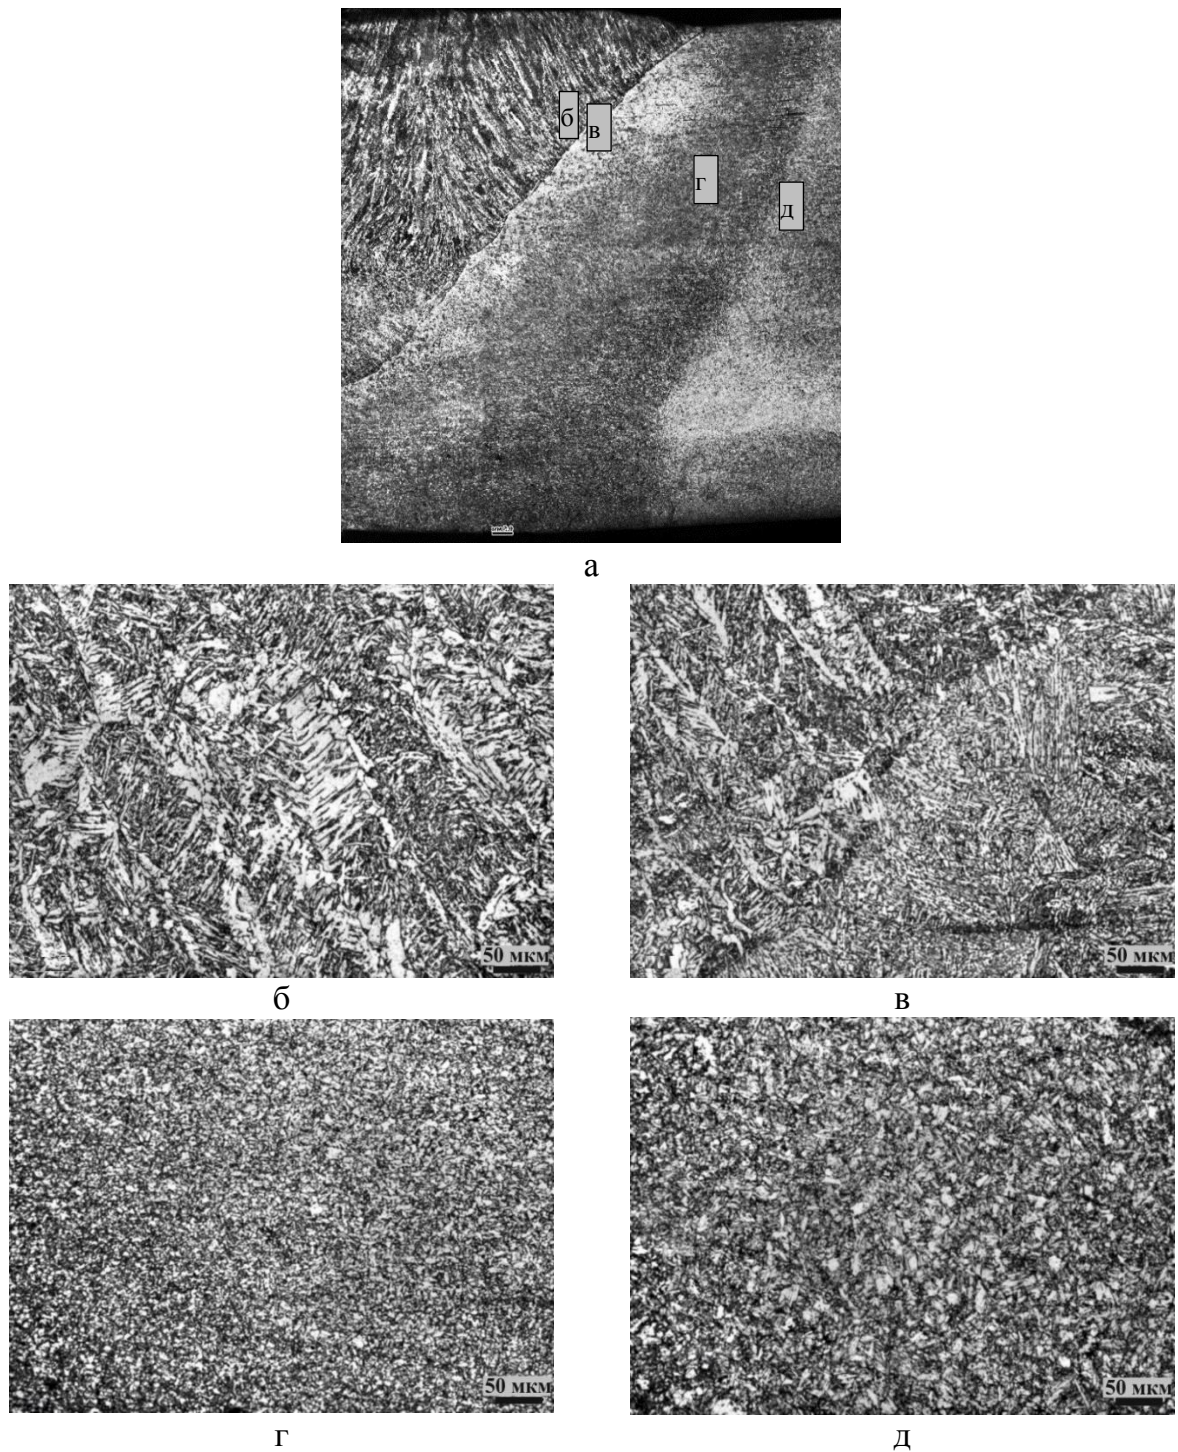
Общий вид сварного соединения (а), структура металла шва (б) и различных участков зоны термического влияния сварного стыкового соединения, полученного электродуговой сваркой:
